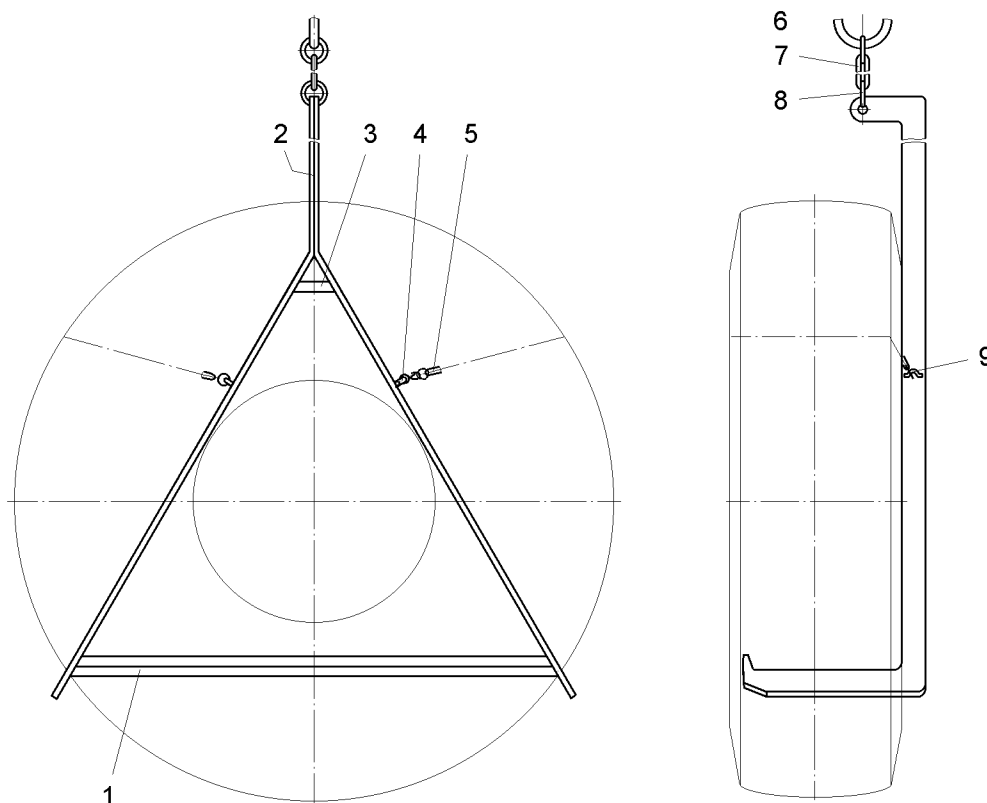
Подвеска для снятия и установки передних и задних колес:
